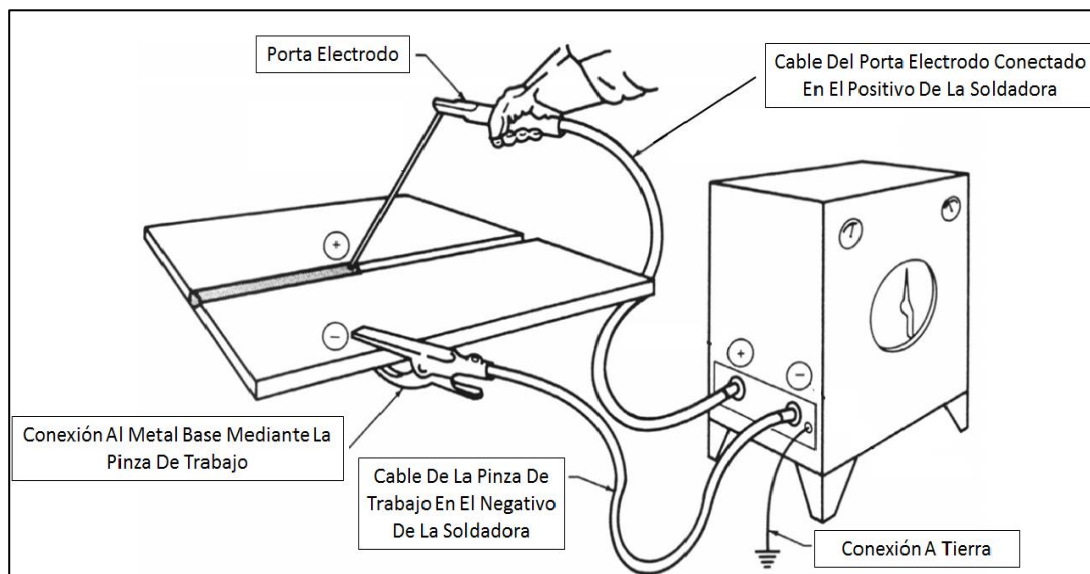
Soldadura En Polaridad Invertida [3].
